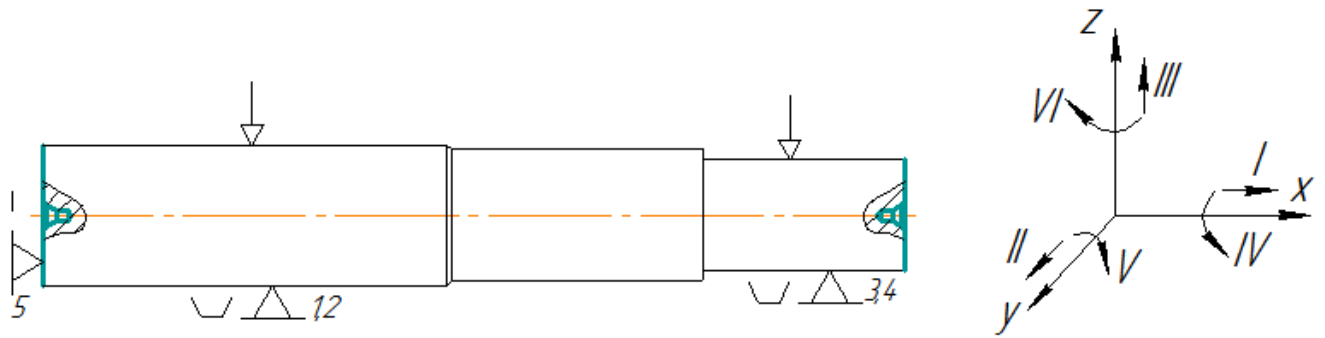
Перший спосіб базування та закріплення заготовки
